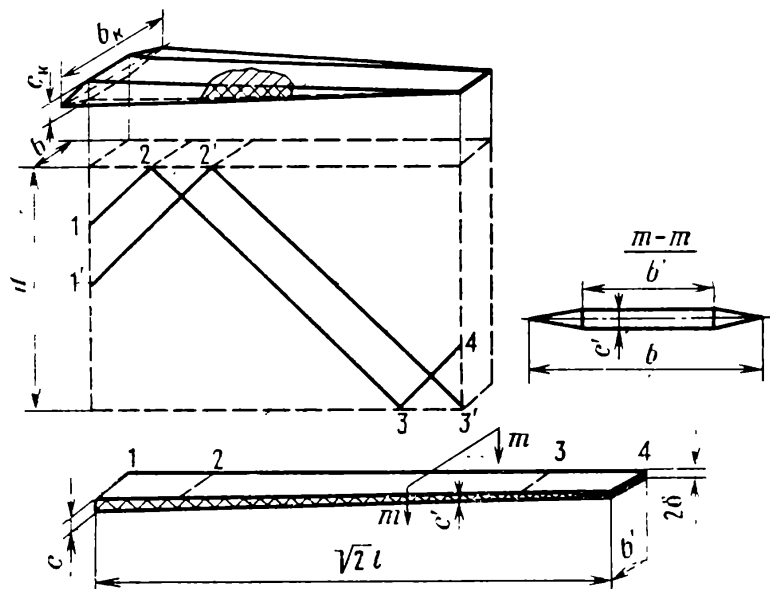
Схема формирования силовой конструкции решетчатого крыла с переменной толщиной планов
